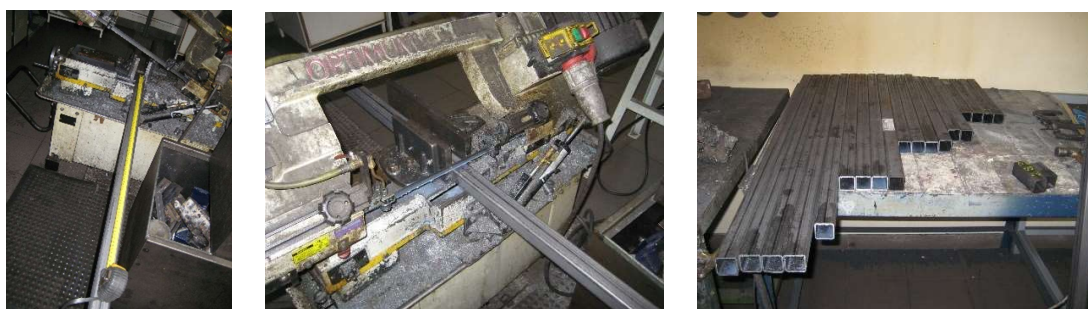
Corte do tubo para a construção do carrinho de suporte
